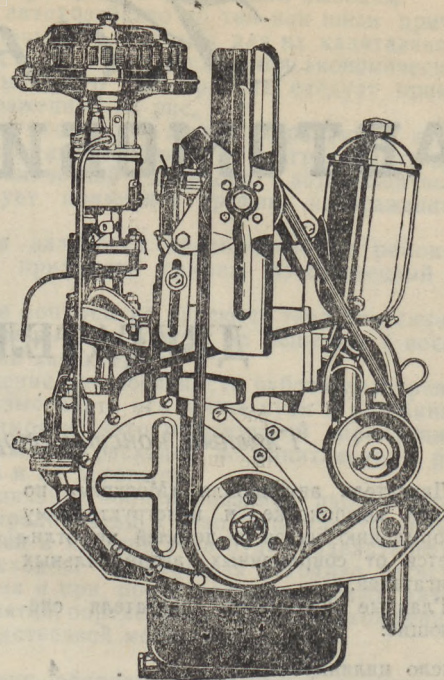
Двигатель автомобиля «Москвич» (вид спереди).
